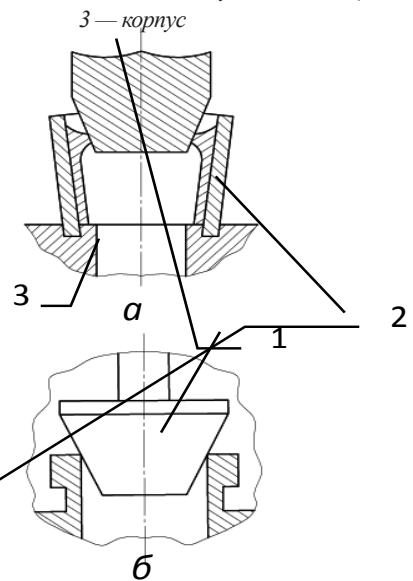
Конструкція метал-металевого затвора з пружними сідлами-втулками: 1 — золотник, 2 — сідло з пружною втулкою, 3 — корпус
